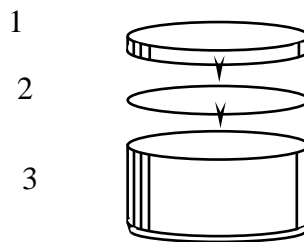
Схема різця: 1 – ріжучий елемент типу 2530 NS; 2 – твердий припой; 3 – циліндр з карбиду вольфраму
